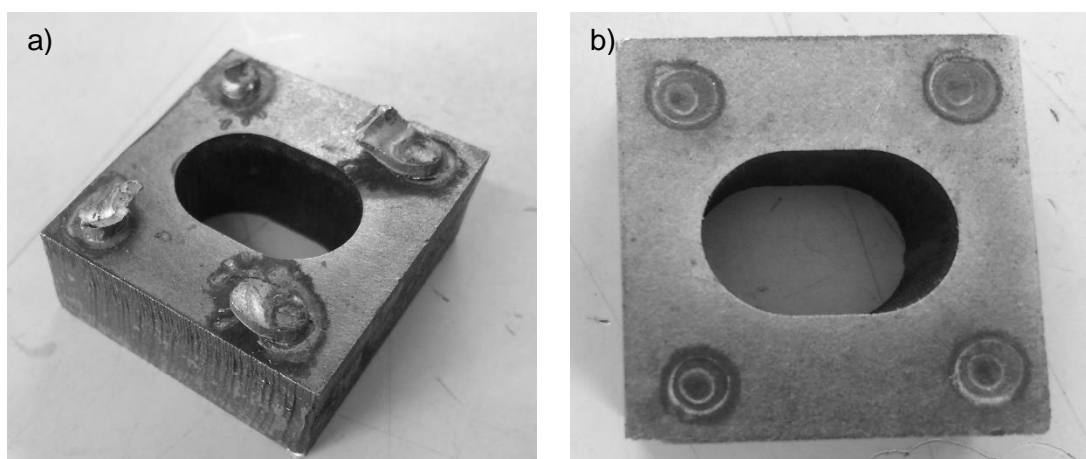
Resultado de uma (a) boa soldadura (OK); e (b) má soldadura (NOK).
